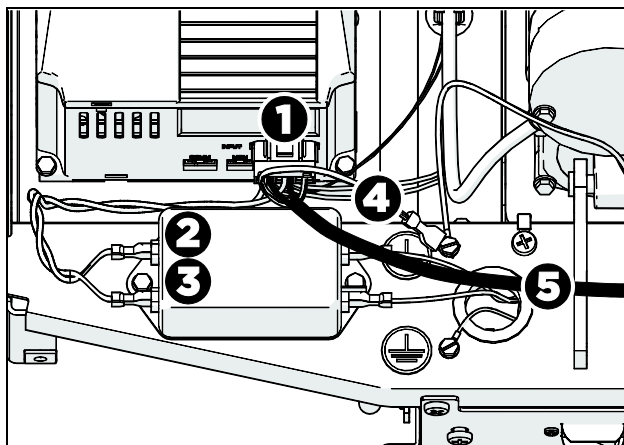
Punti di collegamento del cablaggio di alimentazione dei modelli con console P80
